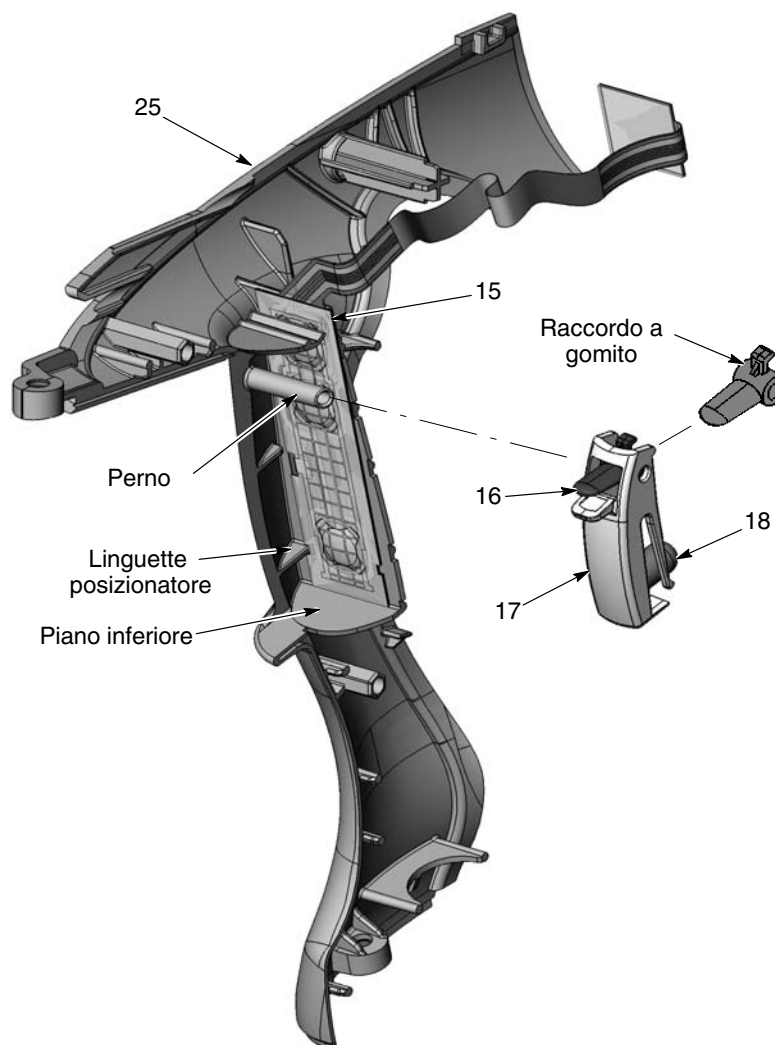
Montaggio dell'interruttore grilletto e del grilletto
